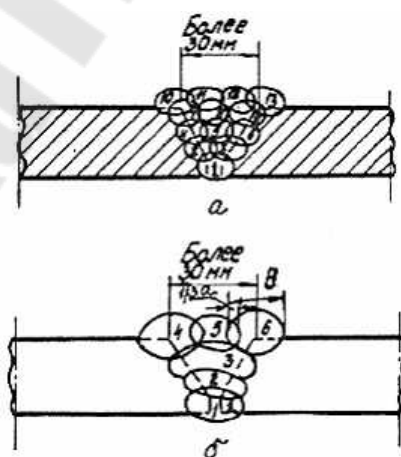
Схема выполнения заполняющих и облицовочного (а), только облицовочного (б) слоев шва несколькими валиками:
